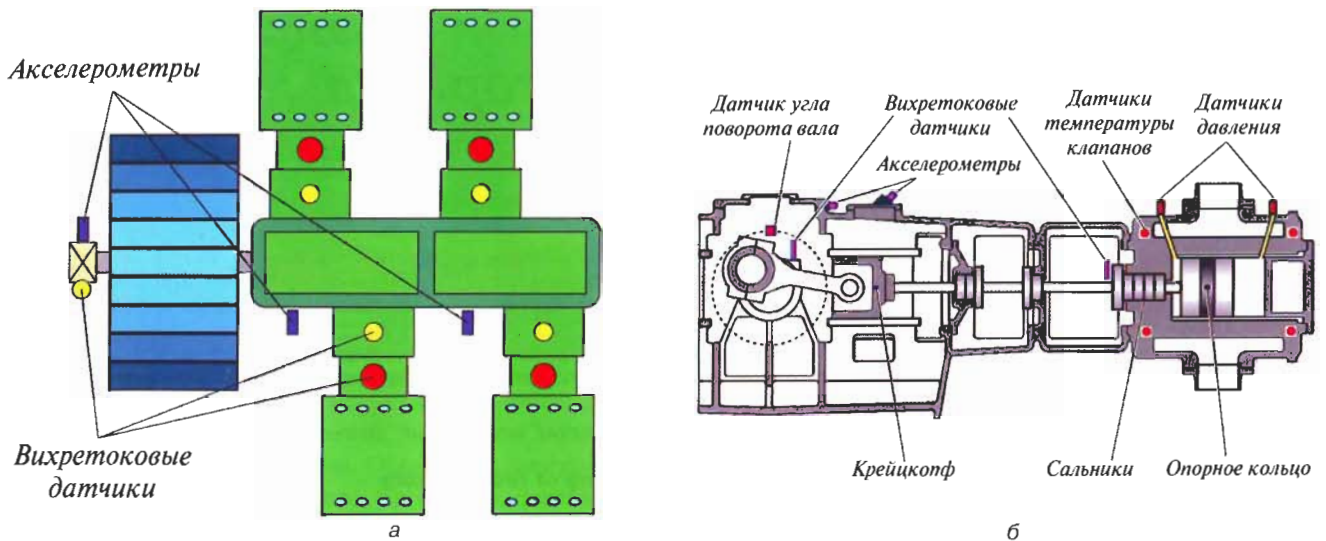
Типовые места установки датчиков на корпусе ПК:
